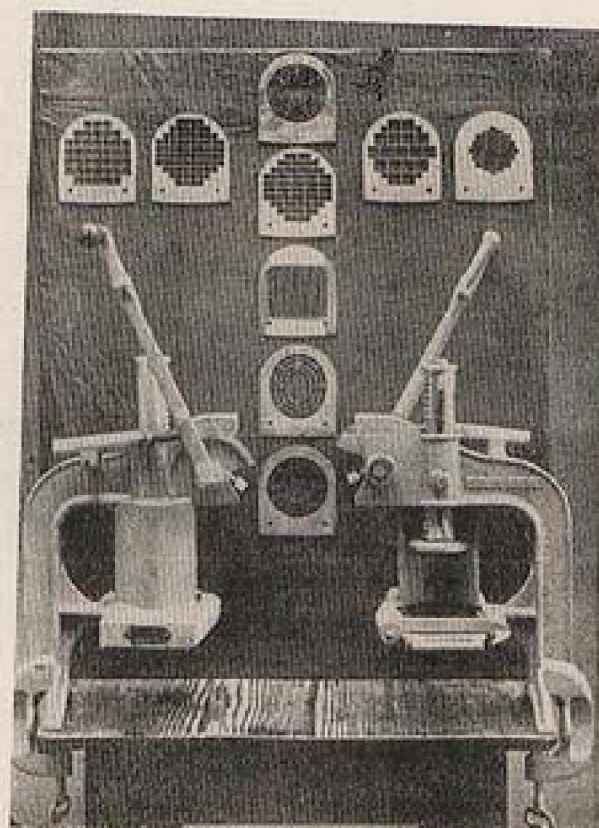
Machines Barbey avec divers modèles de grilles.
